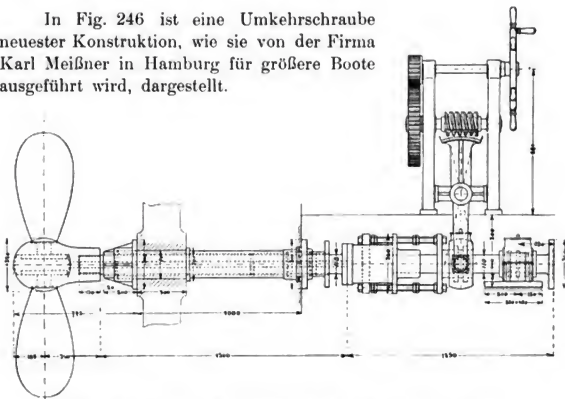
Umkehrschraube für größere Boote von Karl Meißner in Hamburg.
